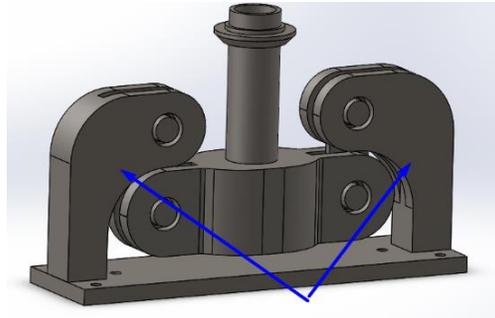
Columna de soporte de péndulo (Pieza N° 9 de ensamble). Fuente: Elaboración propia.
